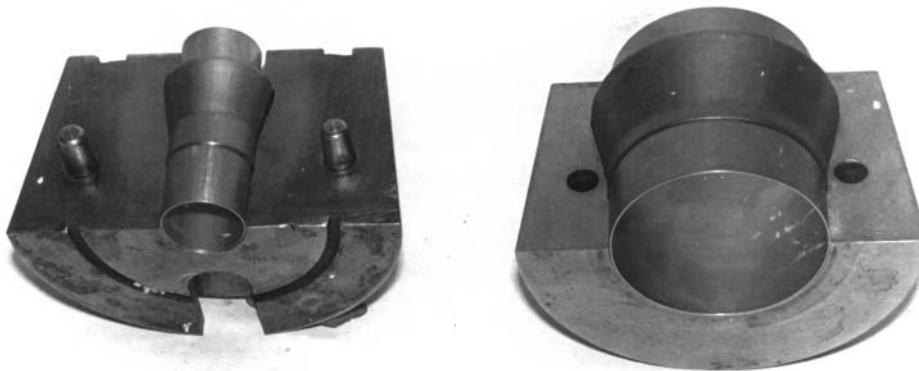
Оснастка и заготовки наконечника конусного усиленного перед вторым переходом
